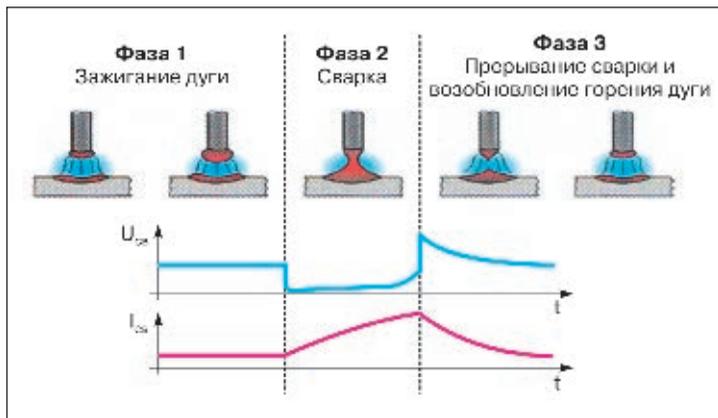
Горение дуги и параметры дуговой сварки
